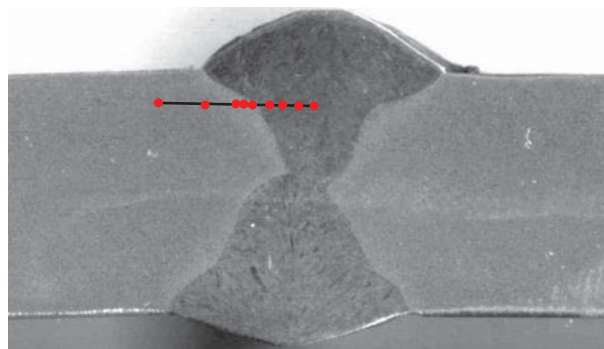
16 La medición de dureza se realizado en el primer cordón de soldadura.
